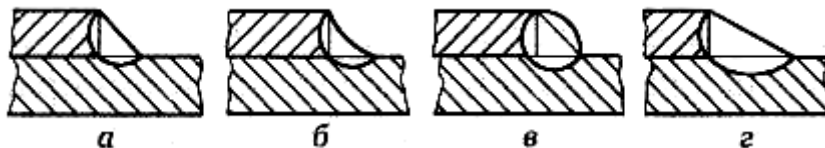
Виды сварных соединений и сварных швов
